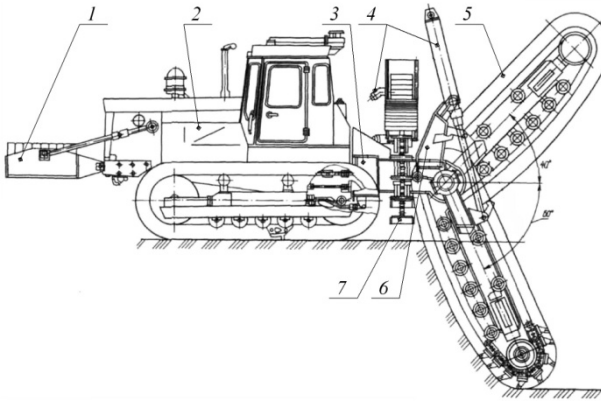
Экскаватор-траншеекопатель ЭТЦ-208В: 1 – противовес; 2 – трактор базовый; 3 – редуктор привода; 4 – гидросистема; 5 – рабочее оборудование; 6 – рама; 7 – поперечный скребковый конвейер
